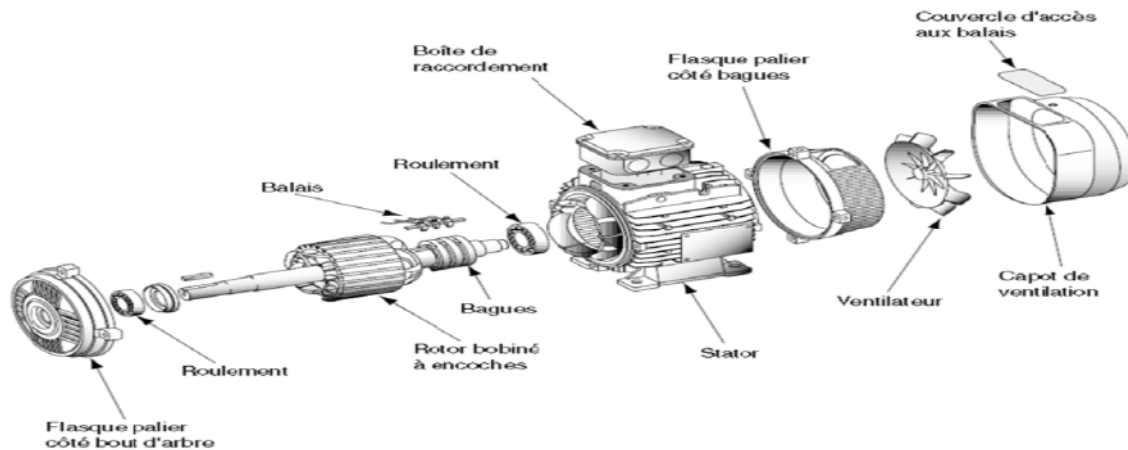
Vue éclatée d'une machine asynchrone à rotor bobiné [10]
